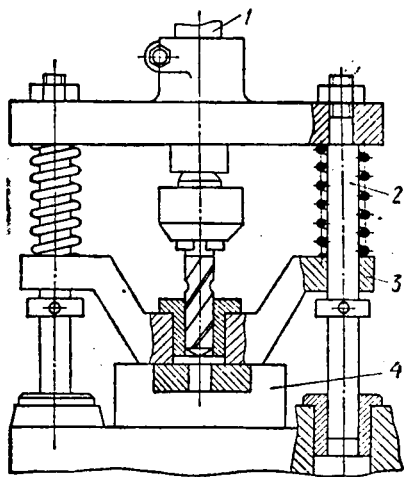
Схема автоматизированного пружинного зажима заготовки в сверлильном приспособлении
